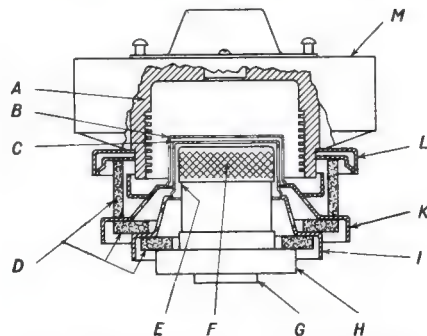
Schnittzeichnung der UHF-Tetrode 7213
